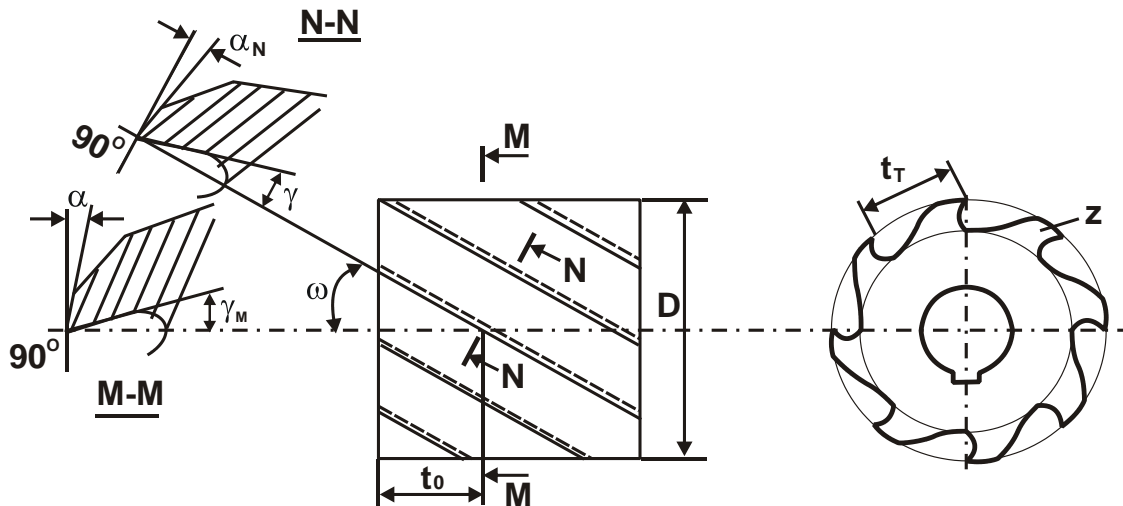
Загальний вигляд осьової циліндричної фрези та її конструктивних елементів
